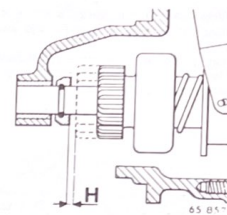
Reglaje del piñón de acoplamiento del motorcito de arranque.
